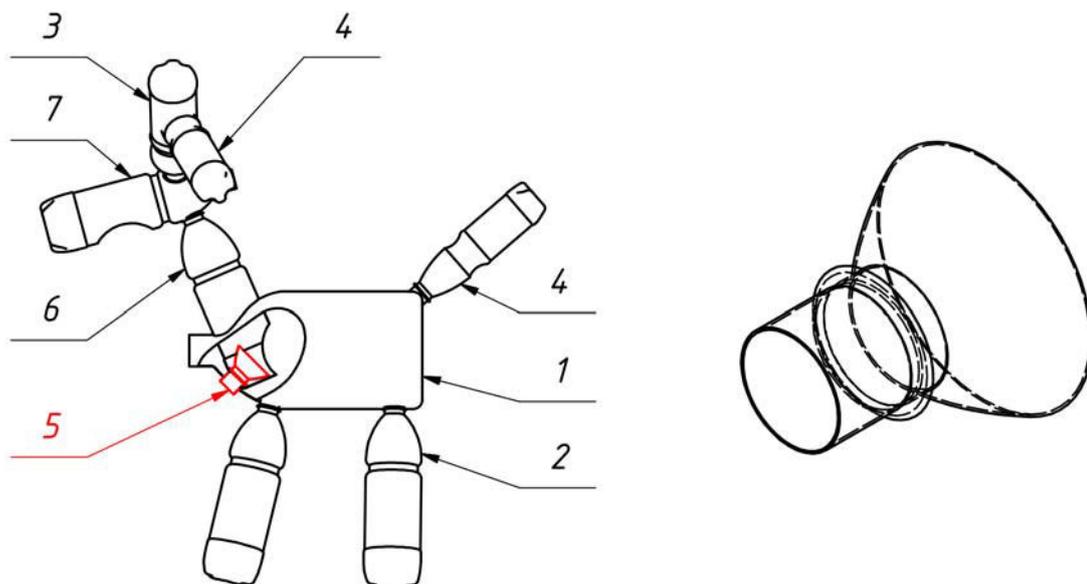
Подготовка детали «крепёж шеи» (поз. 5)
